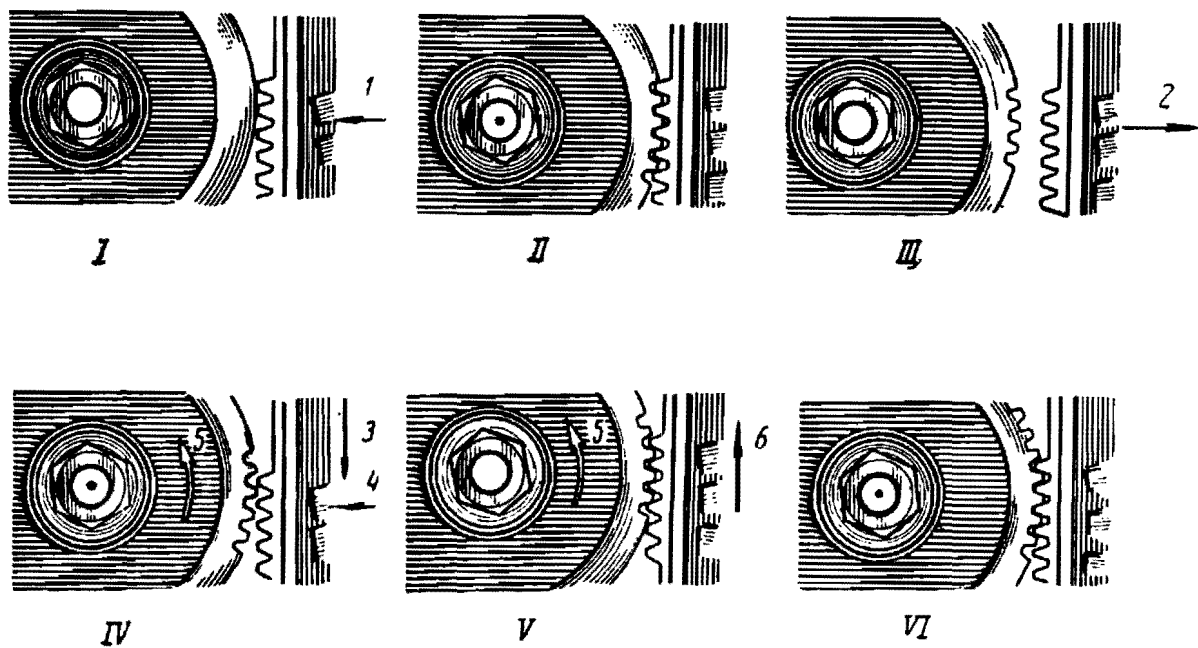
Схема нарезания зубчатого колеса гребенкой на станке типа Паркинсон
